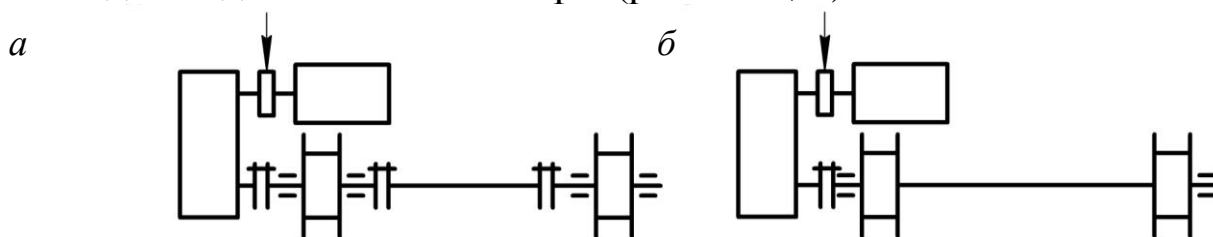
Механизм передвижения тележки с боковым расположением редуктора: а – с валом-вставкой; б – с общей осью
